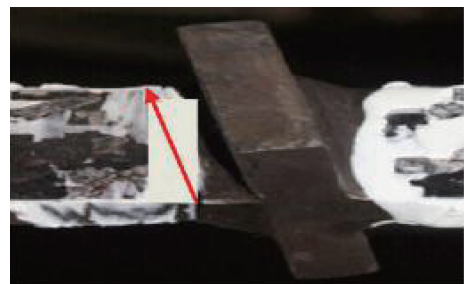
Q345qC 钢全熔透斜焊缝十字接头疲劳试验中裂纹萌生和扩展^[20]
